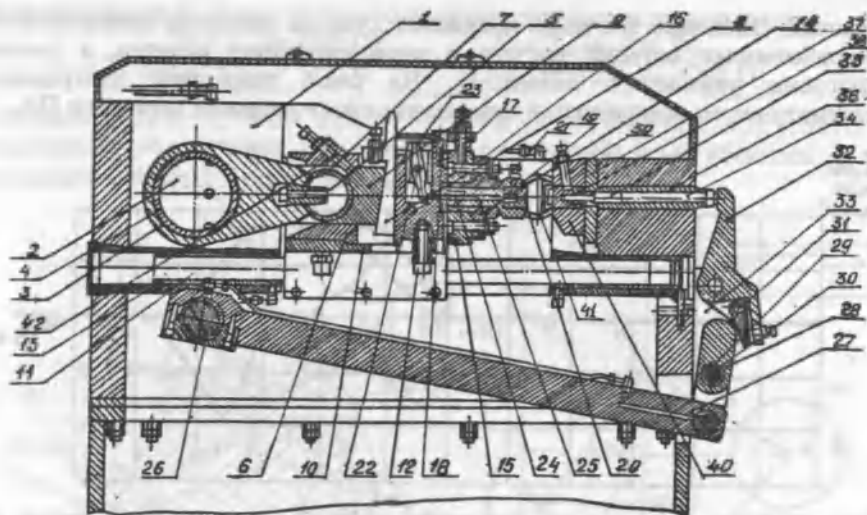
Конструкция шарикоштамповочного пресса-автомата для штамповки шариков с диаметрами 3,0 - 6,0 мм. Где обозначены: 1 - станина; 2 - кривошип; 3, - шатун; 4, 36, 38 - втулки; 5 - палец; 6 - башмак; 7 - регулировочный вкладыш; 8 - конусовидный клин; 9 - центральный ползун; 10 - площадка; 11 - направляющие колонны; 12, 16, 18, 21, 39, 41 - винты; 13, 29 - подшипники скольжения; 14 - пуансонодержатель; 15 - плита; 17 - кронштейн; 19 - пуансон; 20 - рабочий инструмент; 22, 30 - оси; 23 - двухплечный рычаг; 24 - толкатель; 25 - выталкиватель; 26 - эксцентриковый вал; 27 - тяга; 28 - коромысло; 31 - планка; 32 - двухплечный рычаг; 33 - кронштейн станины; 34 - подпружиненный шток; 35 - толкатель; 37 - вставка; 40 - плита; 41 - отрезной нож.
